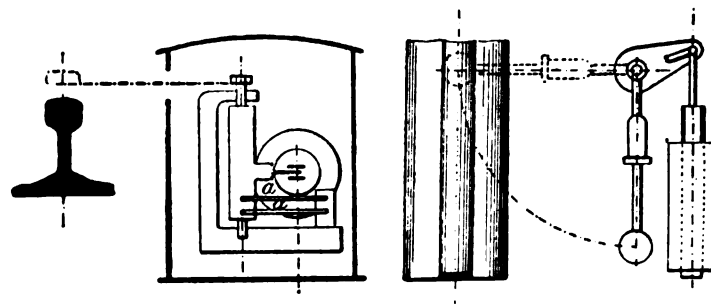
e 5. — Posa-petardi elettrico. Elevazione e pianta.
